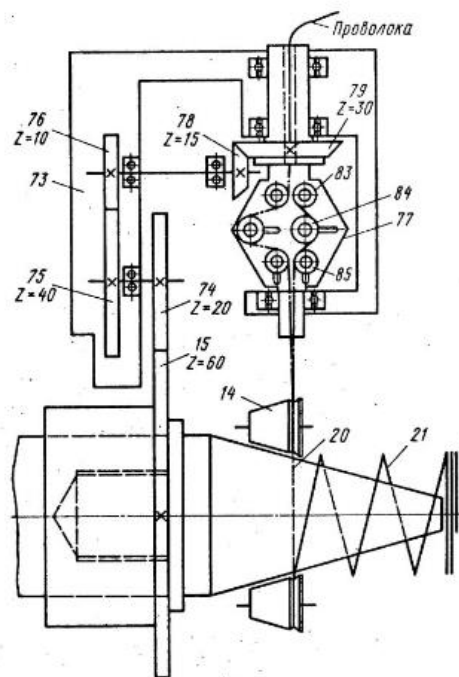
приспособление для навивки конической пружины на токарном станке
